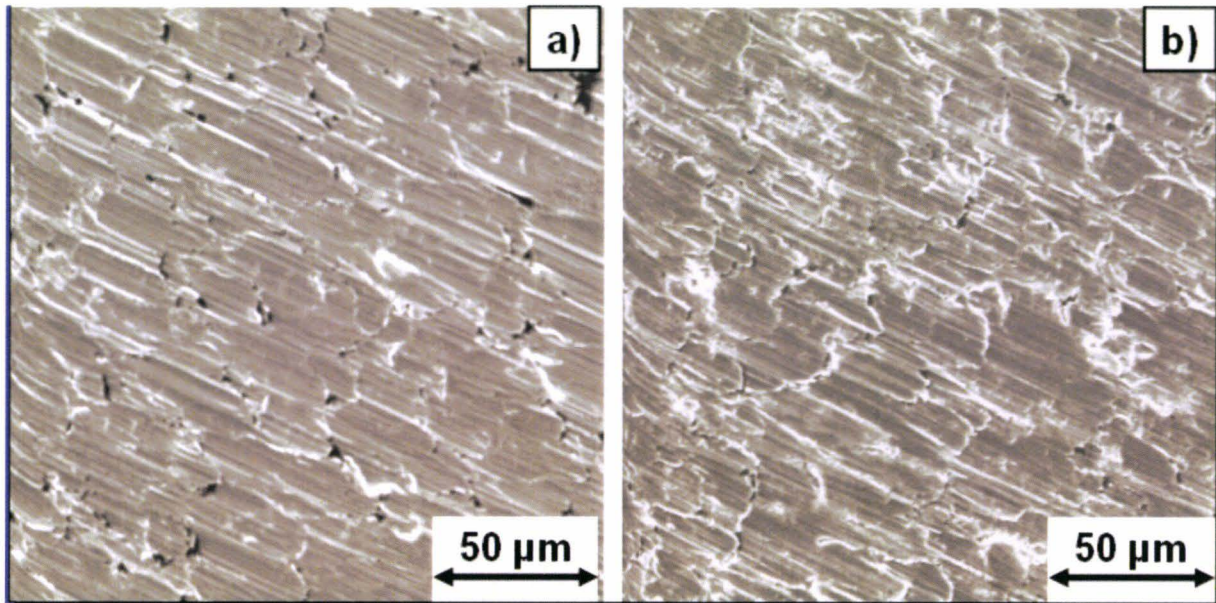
Photographies MEB de tôles laminées expérimentalement après 2 passes pour un glissement en avant de 7% à a) 40°C b) 120°C.
